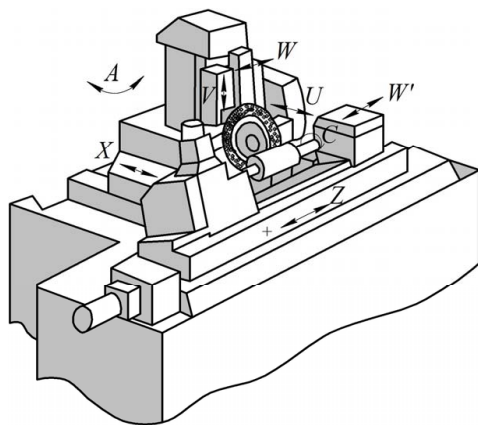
Направления движений рабочих органов резьбошлифовального станка RG500
